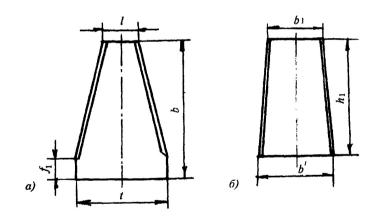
Размеры режущего аппарата: a — сегмент; δ — противорежущая пластина
